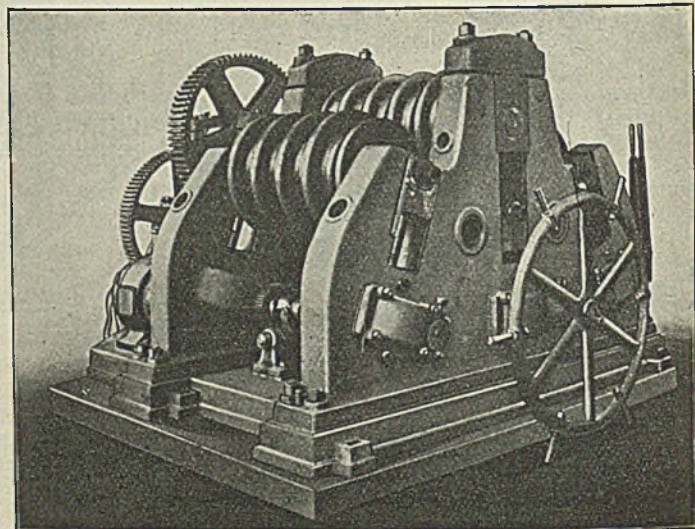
Wellblech-Egalisier- und Bombiermaschine für Doppelwellbleche.
